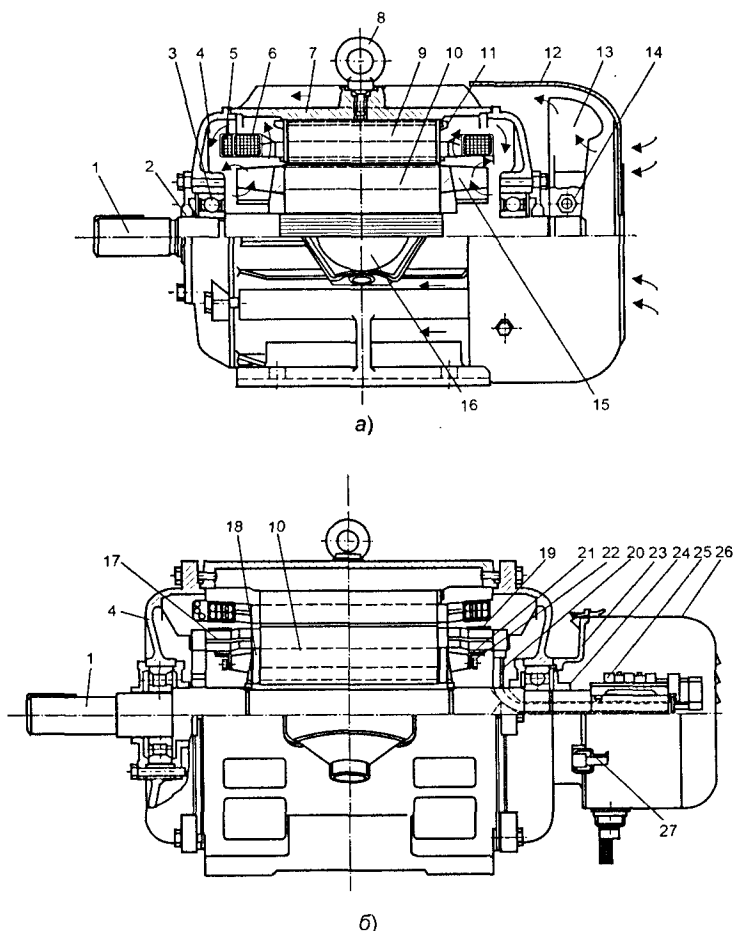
Асинхронные электродвигатели второй единой серии: *а* — АО2-41; *б* — АК2-81; 1 — вал; 2 — крышка подшипника; 3 — подшипник; 4 — подшипниковый щит; 5 — выводные провода обмотки статора; 6 — катушка однослойной обмотки статора; 7 — корпус статора; 8 — подъемное кольцо (рым-болт); 9 — сердечник статора; 10 — сердечник ротора; 11 — скоба, стягивающая пакет сердечника статора; 12 — кожух вентилятора наружного обдува; 13 — вентилятор наружного обдува; 14 — болт крепления ступицы вентилятора на валу; 15 — лопасти вентилятора, перемешивающего воздух внутри машины; 16 — коробка выводов; 17 — обмотка ротора; 18 — нажимная шайба; 19 — бандаж лобовой части обмотки ротора; 20 — вывод от роторной обмотки к контактному кольцу; 21 — кольцо, поддерживающее лобовые части роторной обмотки; 22 — бобышки нажимной шайбы, к которым крепится поддерживающее кольцо; 23 — диск, на котором крепится ось щеткодержателя; 24 — наружная крышка подшипниковой камеры (прижимается диском 23); 25 — контактные кольца; 26 — съемный кожух контактных колец; 27 — замок съемного кожуха
